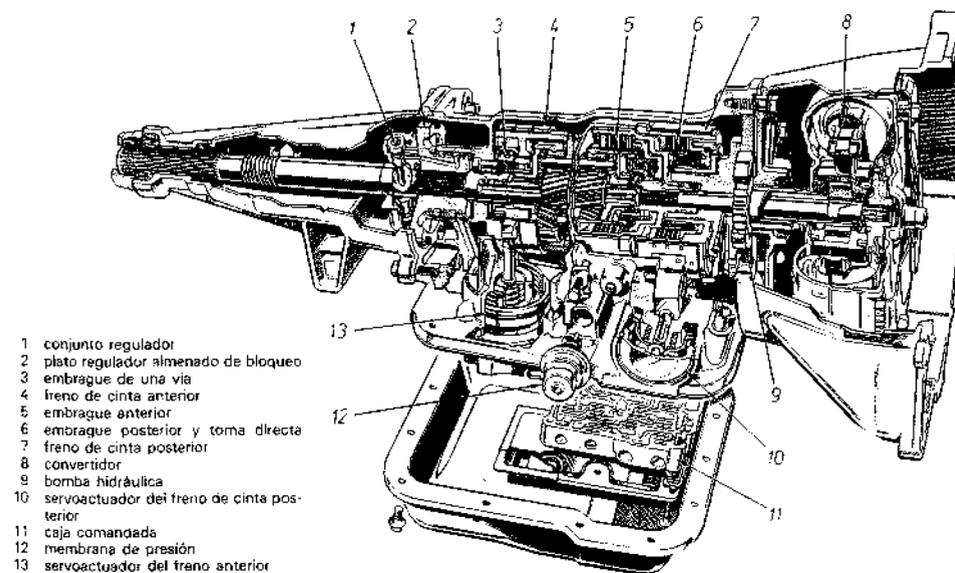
A Vista seccionada de una caja de cambios automática.
